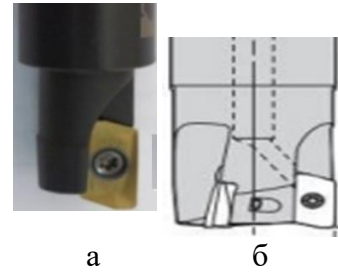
Однозубая фреза с механическим креплением СМП фото (а) и схема с тремя зубьями
